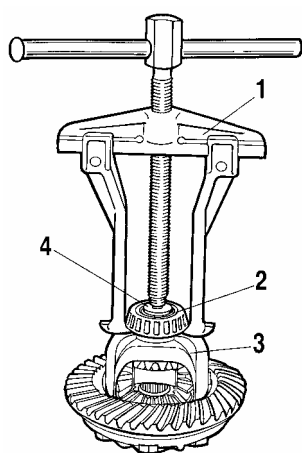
Снятие внутреннего кольца подшипника коробки дифференциала универсальным съемником А.40005/1/6:
